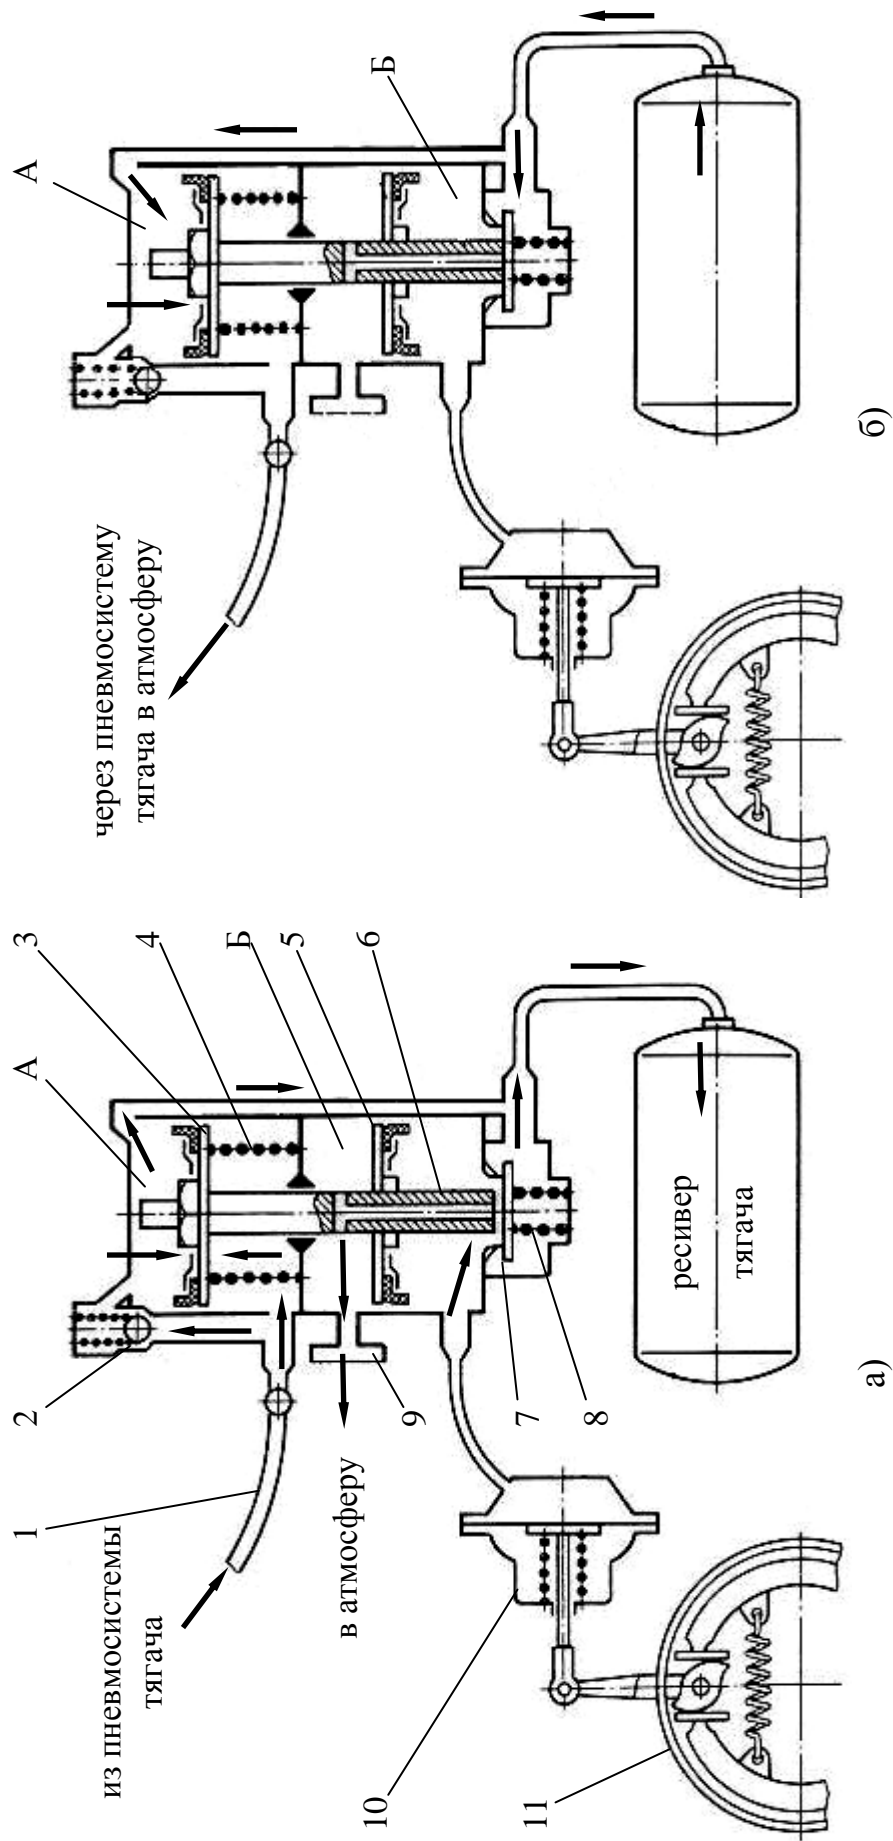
Схема работы воздухораспределителя прицепа при однопроводном приводе тормозной системы: а – торможение отсутствует, б – начало торможения; 1 – соединительная пневмомагистраль тягача и прицепа; 2 – шариковый клапан; 3 – верхний поршень; 4 – пружина верхнего поршня; 5 – нижний поршень; 6 – шток; 7 – пластинчатый клапан; 8 – пружина клапана; 9 – фильтр; 10 – тормозные камеры прицепа; 11 – тормозные механизмы прицепа; А и Б – полости воздухораспределителя
